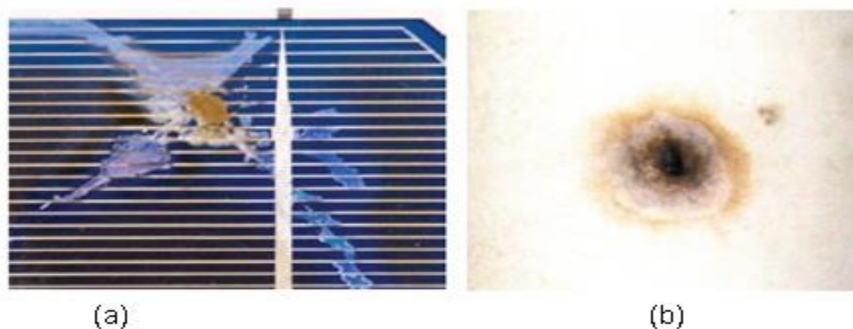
a y b) Módulo con punto caliente; a) parte frontal, b) parte trasera.
